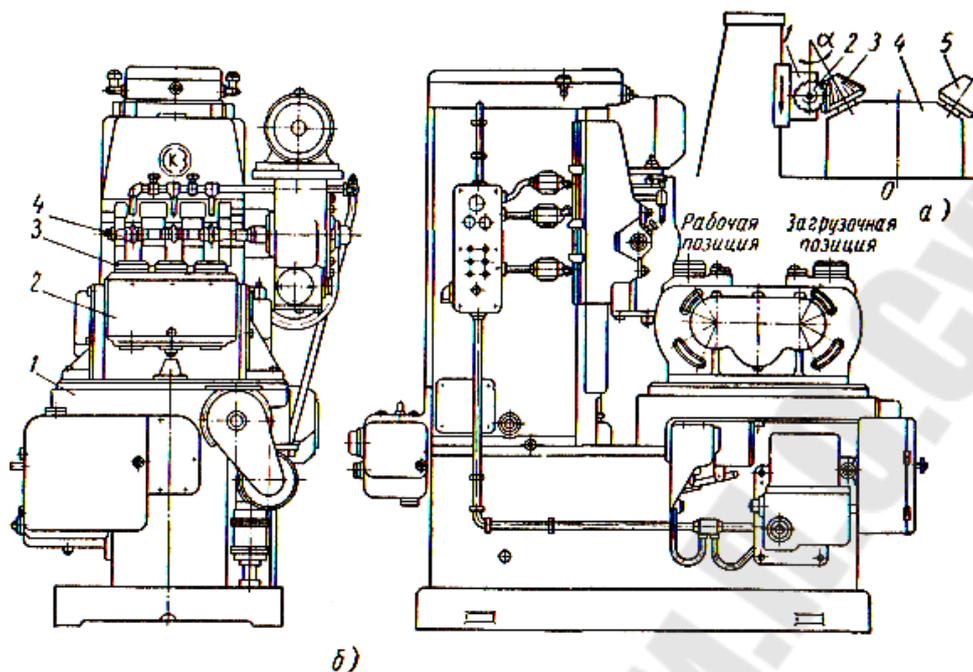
Зубофрезерный полуавтомат для предварительной обработки заготовок прямозубых цилиндрических и конических колес
